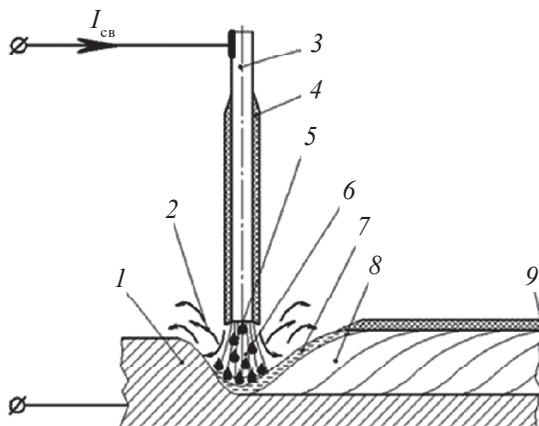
Схема сварки покрытым металлическим электродом:
